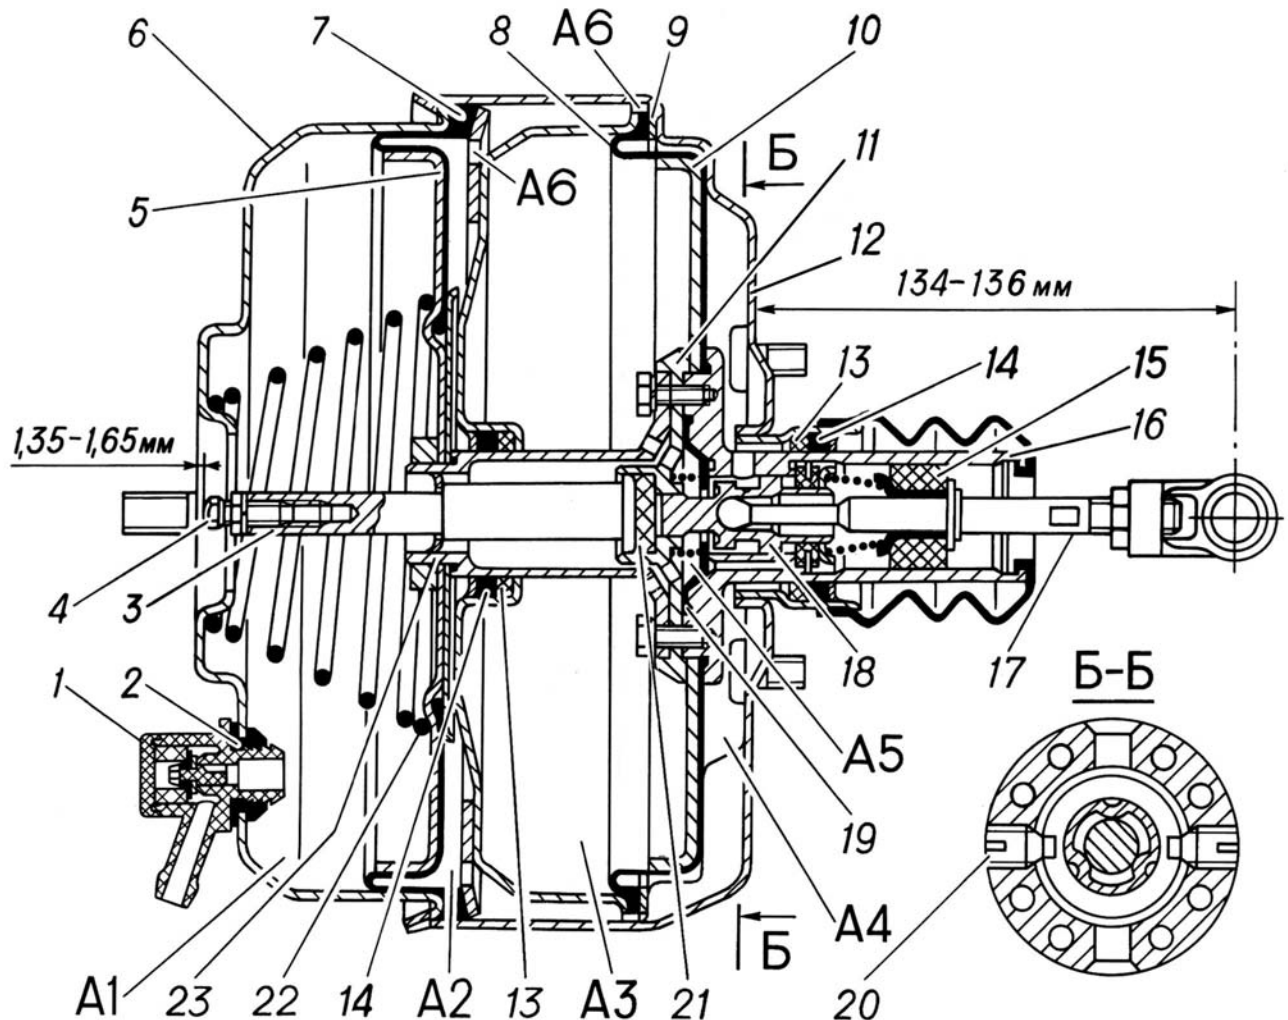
Вакуумный усилитель: A1, A2, A3, A4 и A5 - полости вакуумного усилителя; A6 - отверстия; 1 - обратный клапан; 2 - уплотнительная втулка; 3 и 17 - толкатели; 4 - регулировочный болт; 5, 10 и 18 - поршни; 6 - крышка; 7 и 8 - диафрагмы; 9 - упорное кольцо; 11 - фланец поршня; 12 - корпус усилителя; 13 - направляющие кольца; 14 - уплотнительные манжеты; 15 - фильтр; 16 - корпус клапанов; 19 - диафрагма клапана управления; 20 - винт; 21 - реактивная шайба; 22 - пружина; 23 - соединитель поршней
